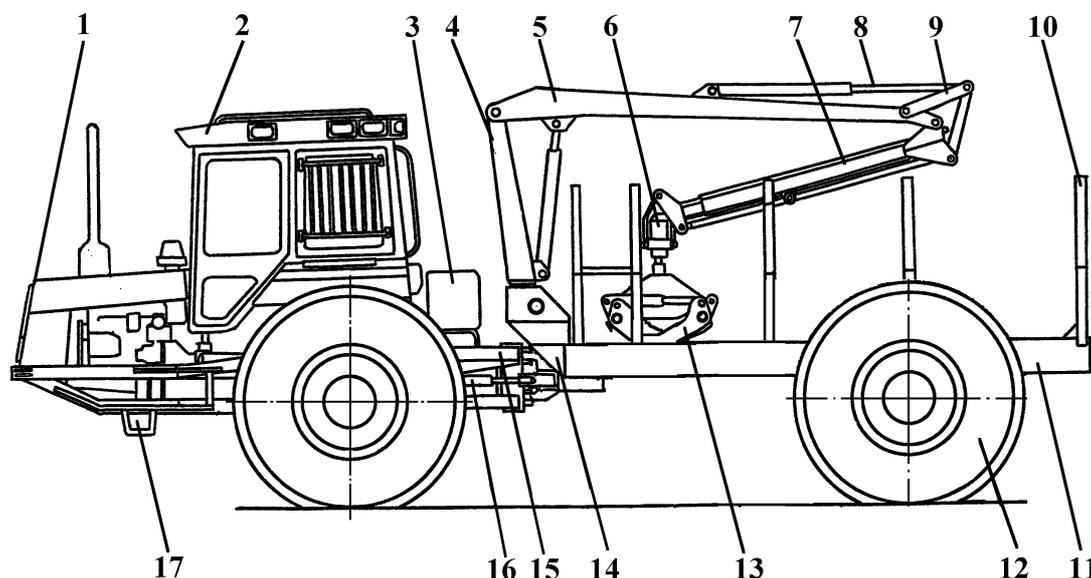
Погрузочно-транспортная машина МЛПТ-354: 1 – двигатель; 2 – кабина; 3 – бак гидропривода; 4 – колонна манипулятора; 5 – стрела манипулятора; 6 – ротатор манипулятора; 7 – рукоятка; 8 – гидроцилиндр управления рукояткой; 9 – четырехзвенник; 10 – стойки коника; 11 – грузовая платформа; 12 – колесо; 13 – грейфер; 14 – опора вертикально-горизонтального шарнира;
